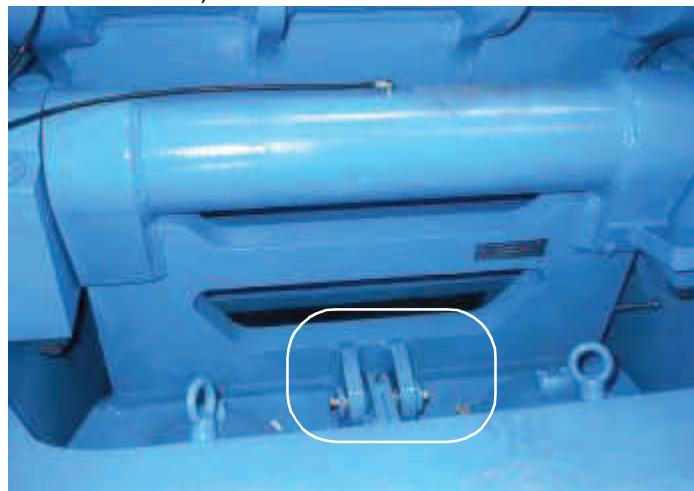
Punto di ingrassaggio sul cilindro tensionatore
